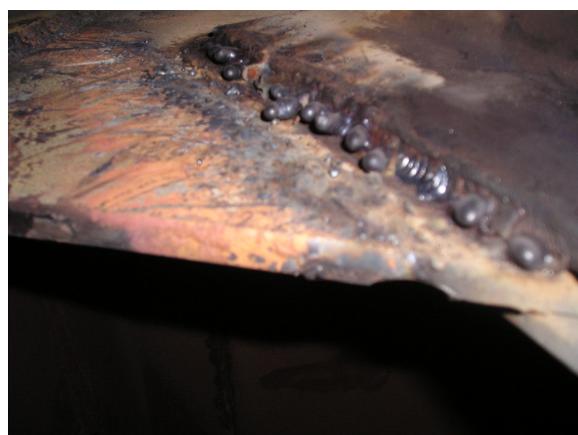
Пример некачественного выполнения сварного шва несущей металлоконструкции пратценкрана обжимного цеха.
